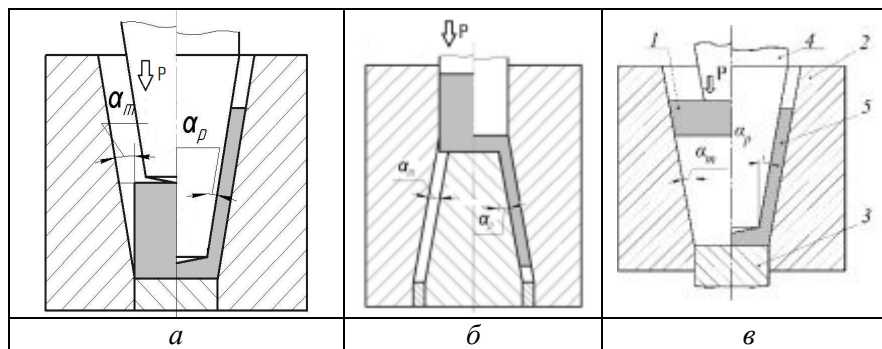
Схеми видавлювання порожнистих деталей типу «конічний стакан»
